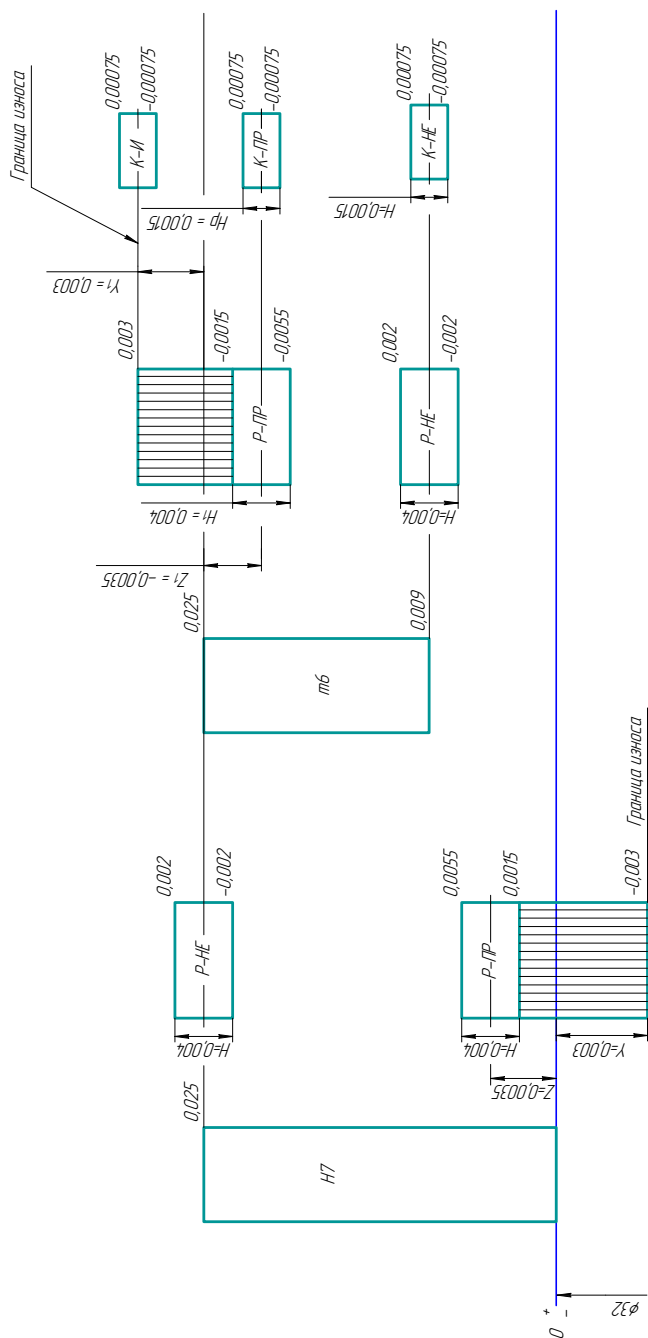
Схема расположения полей и допусков деталей и калибров
